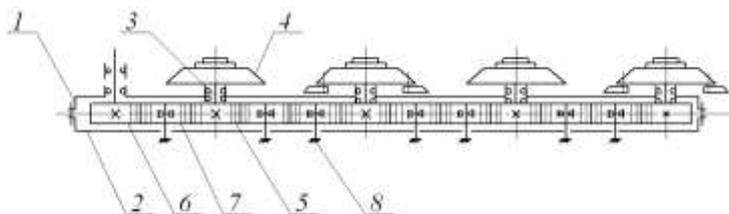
Схема привода роторов от зубчатой цилиндрической передачи
